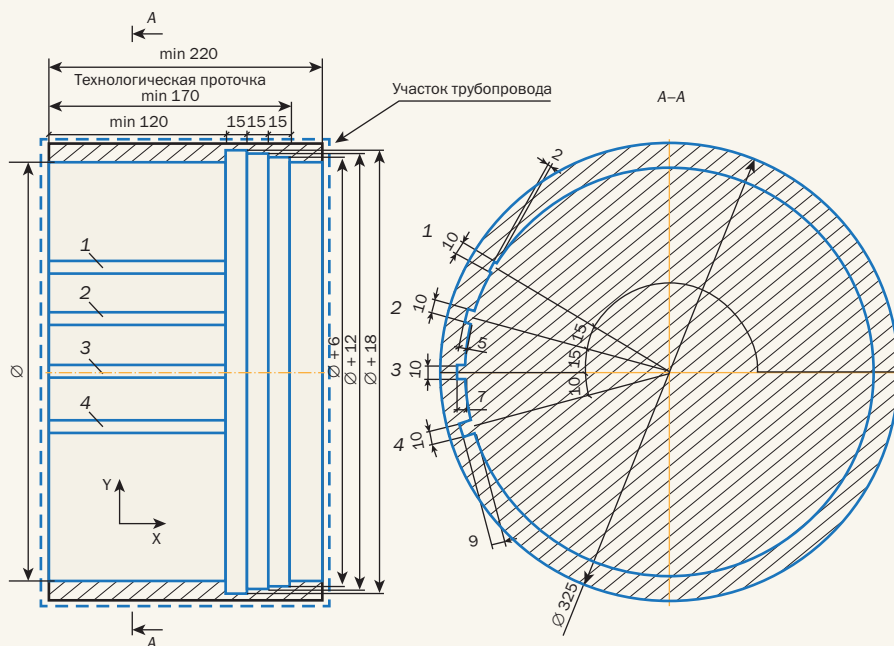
Испытательный образец для прямо-сдаточных испытаний на ЛАЭС
